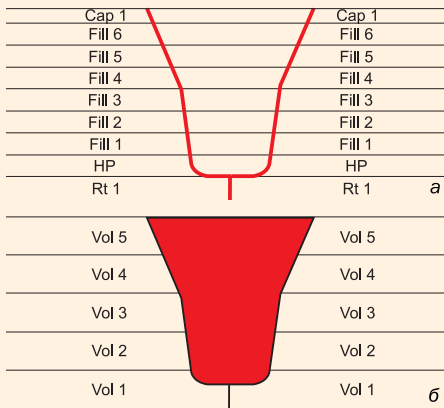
Пример профиля сварного шва и разделение на зоны с целью выявления несплавленной по кромке (а) и обнаружения дефектов в наплавленном металле (б)
